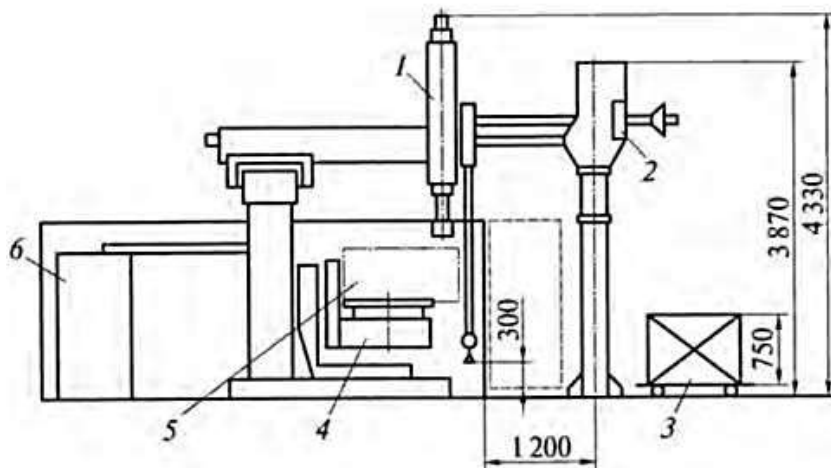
Схема робототехнічного комплексу дугового зварювання:
